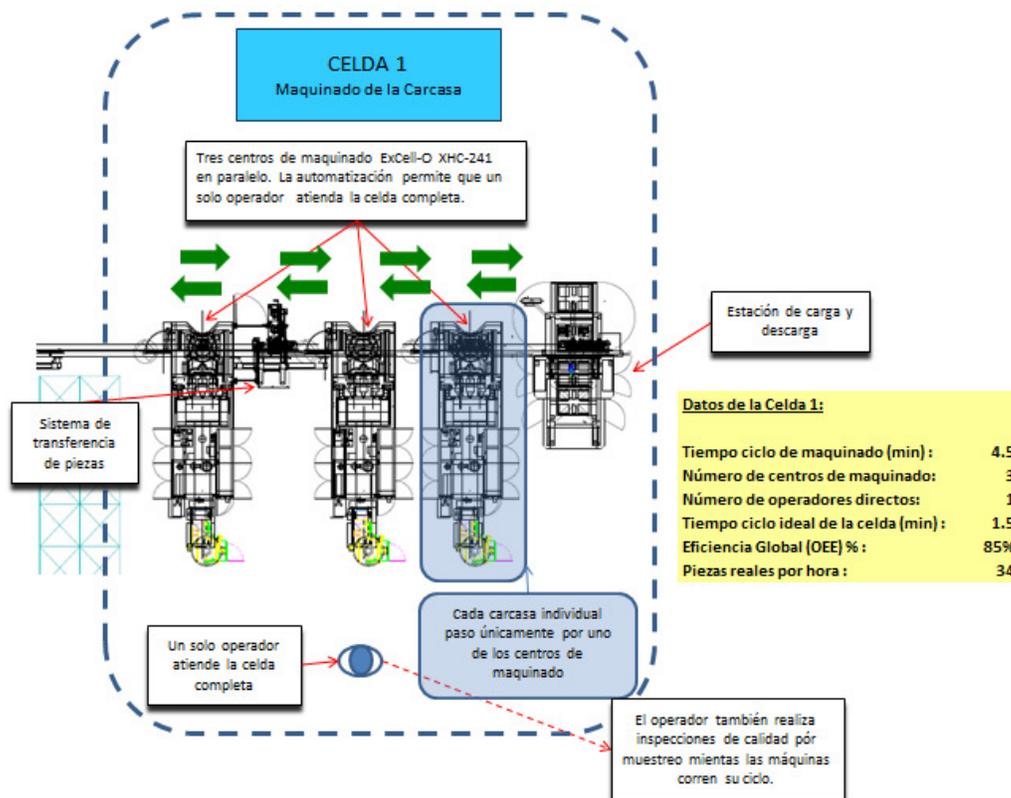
Configuración o layout de la celda de maquinado de la carcasa.
